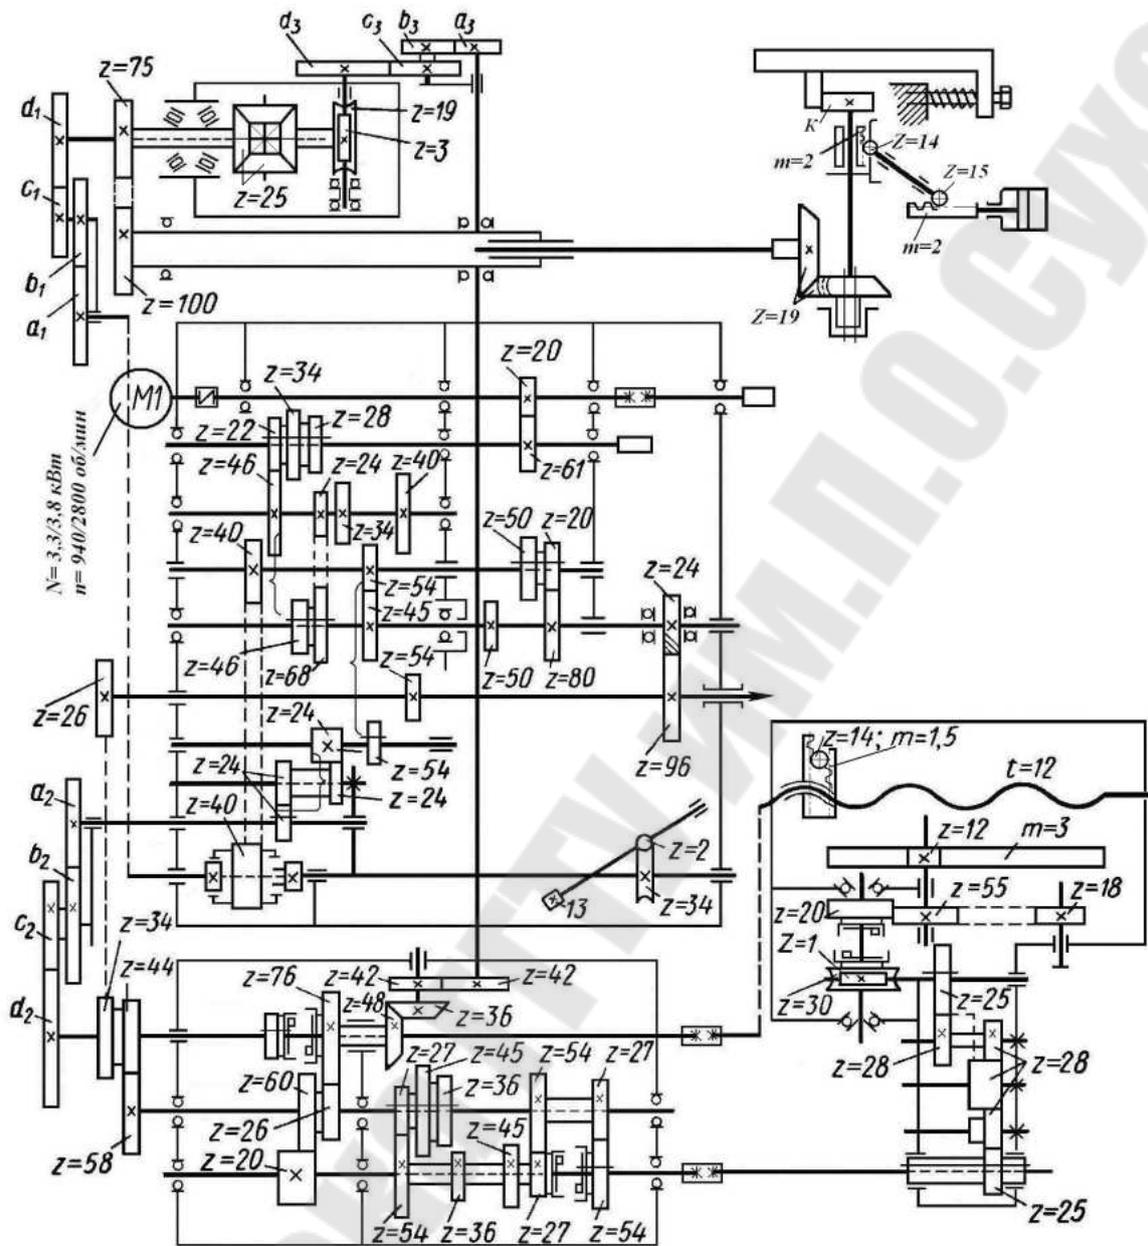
Принципиальная схема токарно-затывловочного станка 1811
